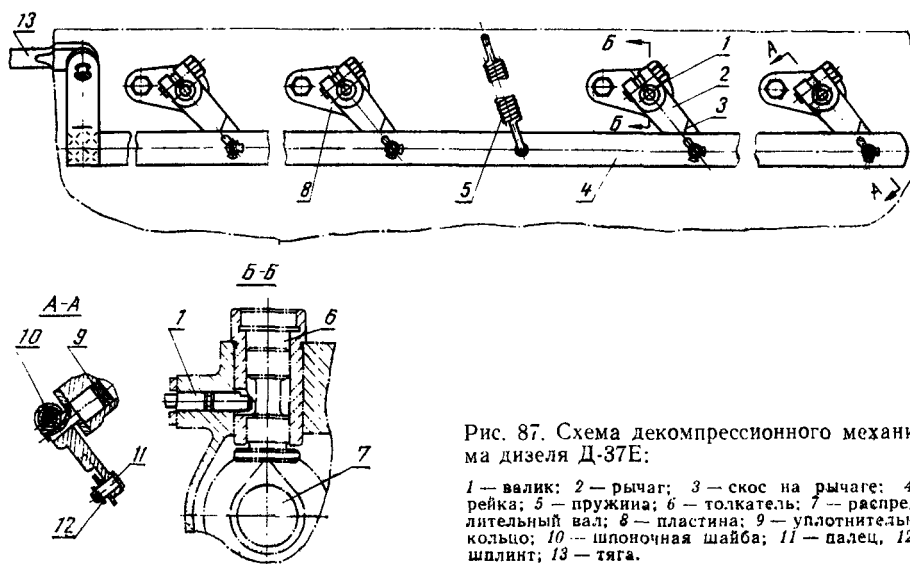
Схема декомпрессионного механизма дизеля Д-37Е:
